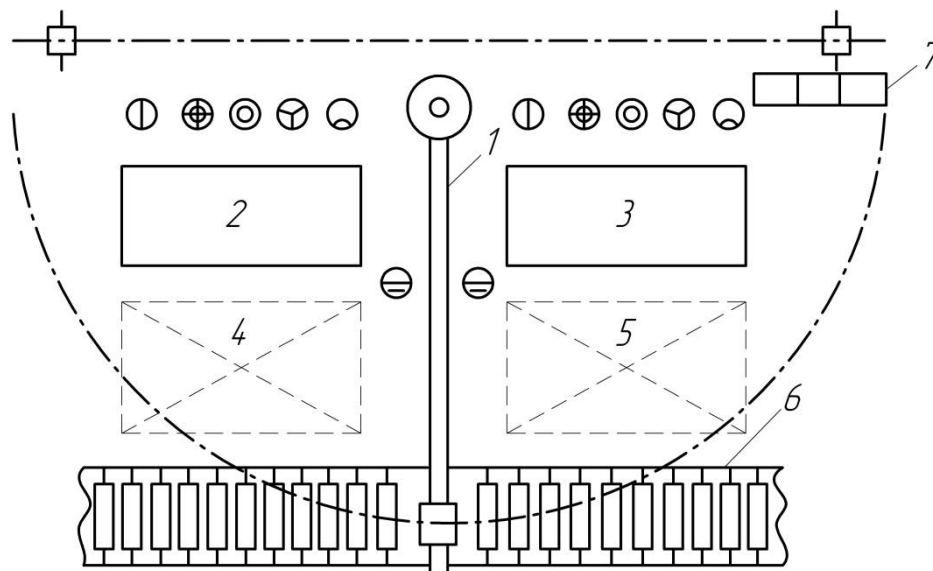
Планировка участка сборки и сварки деталей и сборочных единиц на потоке:
